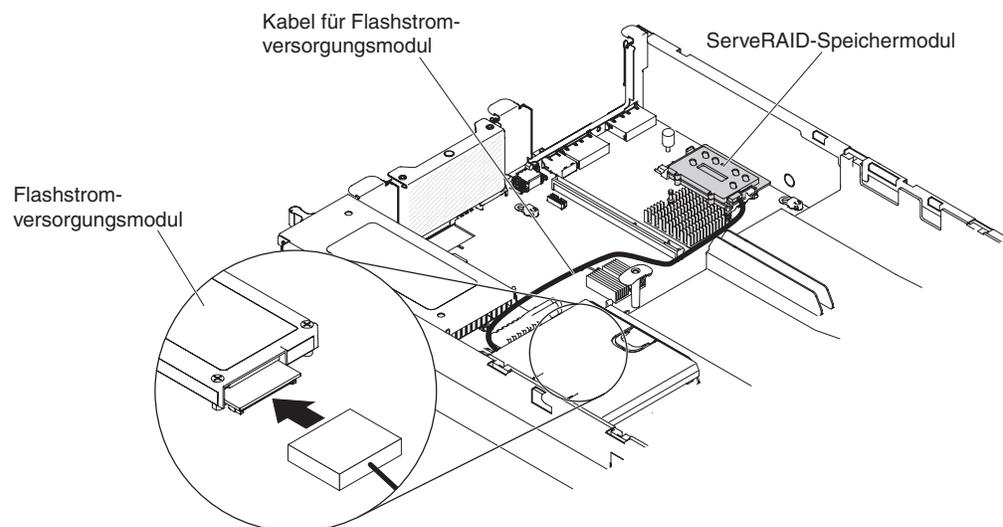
Kabel für Akku oder Flashstromversorgungsmodul installieren
